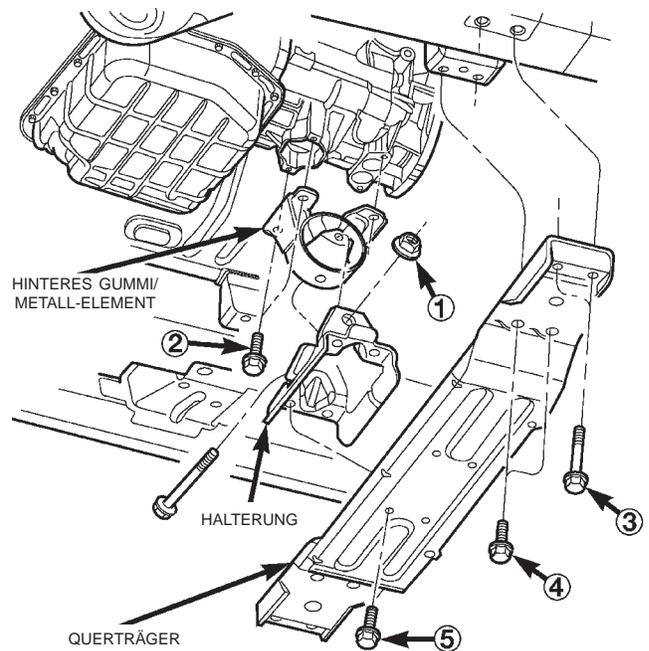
Hintere Motoraufhängung—Allradantrieb
